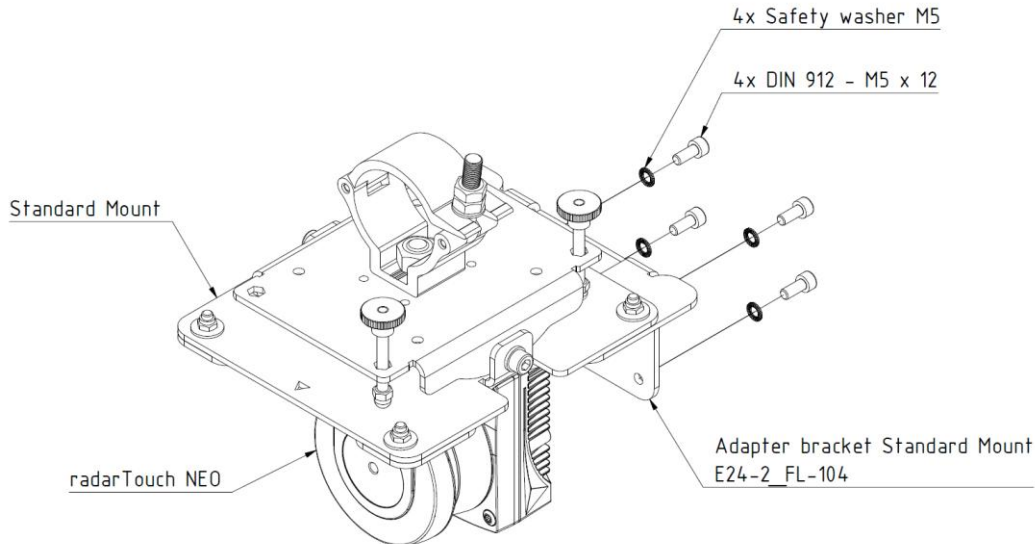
Explosionszeichnung Montage an Standard Mount
